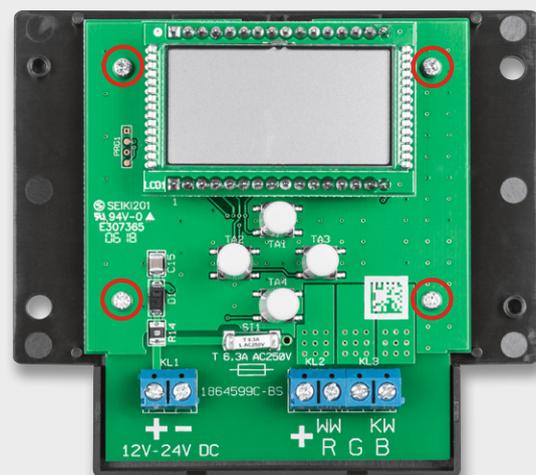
So wird die Hauptplatine mit vier Schrauben im Gehäuseunterteil verschraubt.
